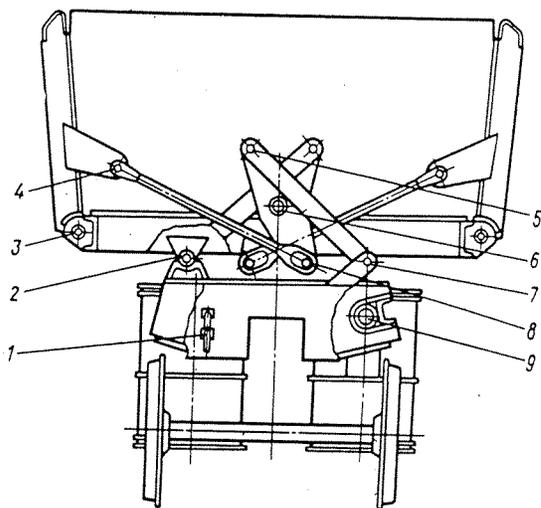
Схема смазки механизма разгрузки и механизма открывания бортов:
